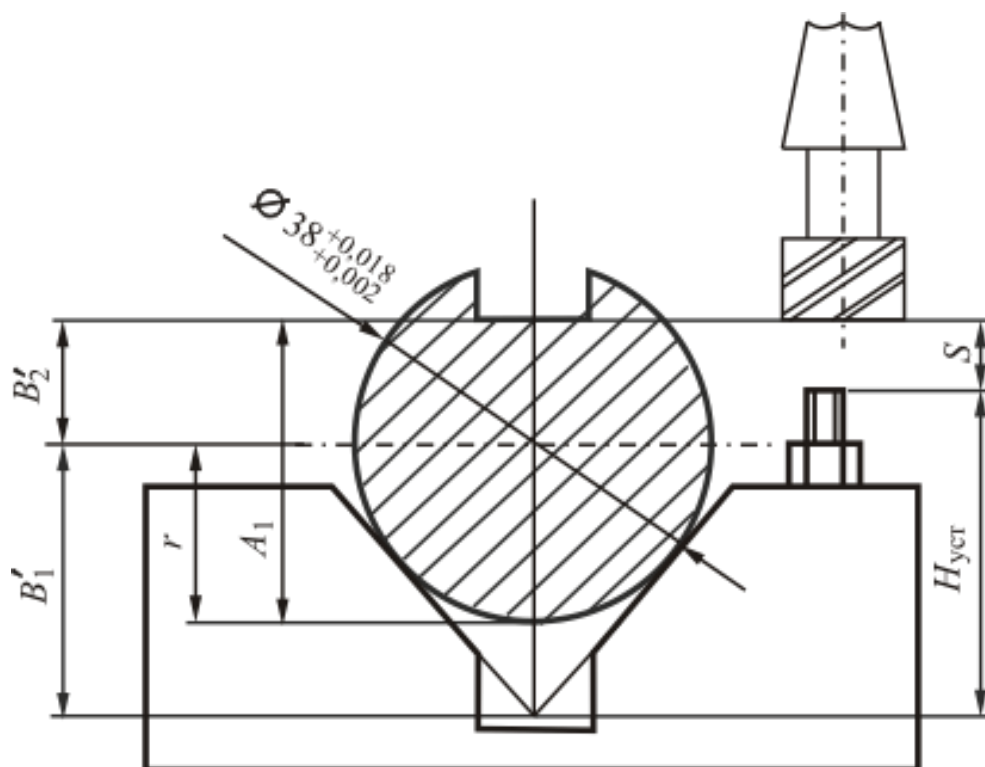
Схема наладки фрезерного станка при обработке в размер A_1
